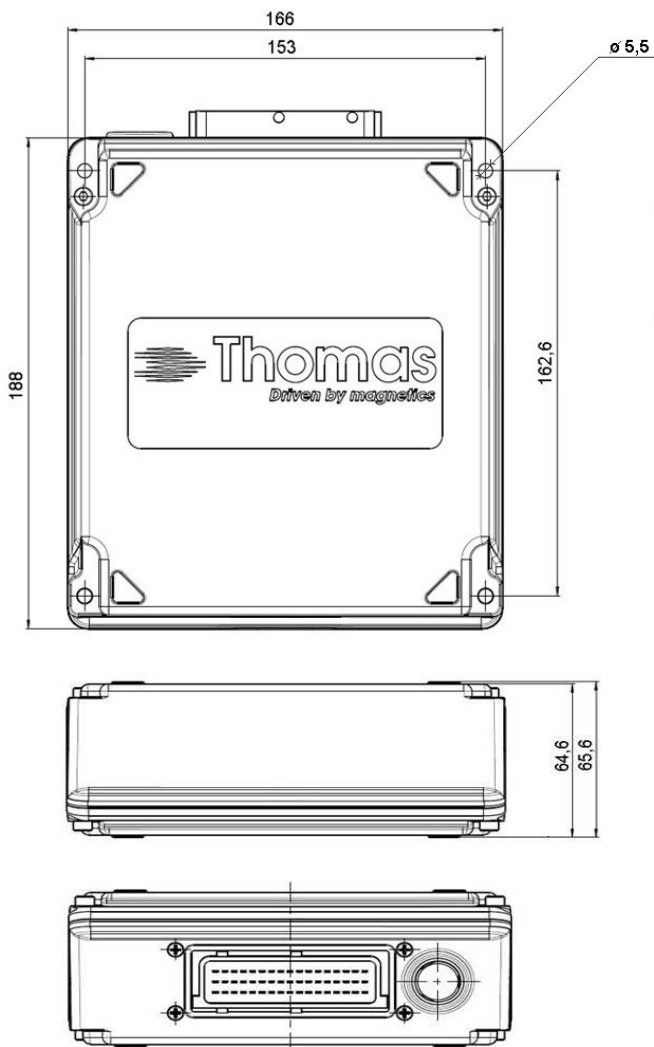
Габаритные и присоединительные размеры БЭУ
